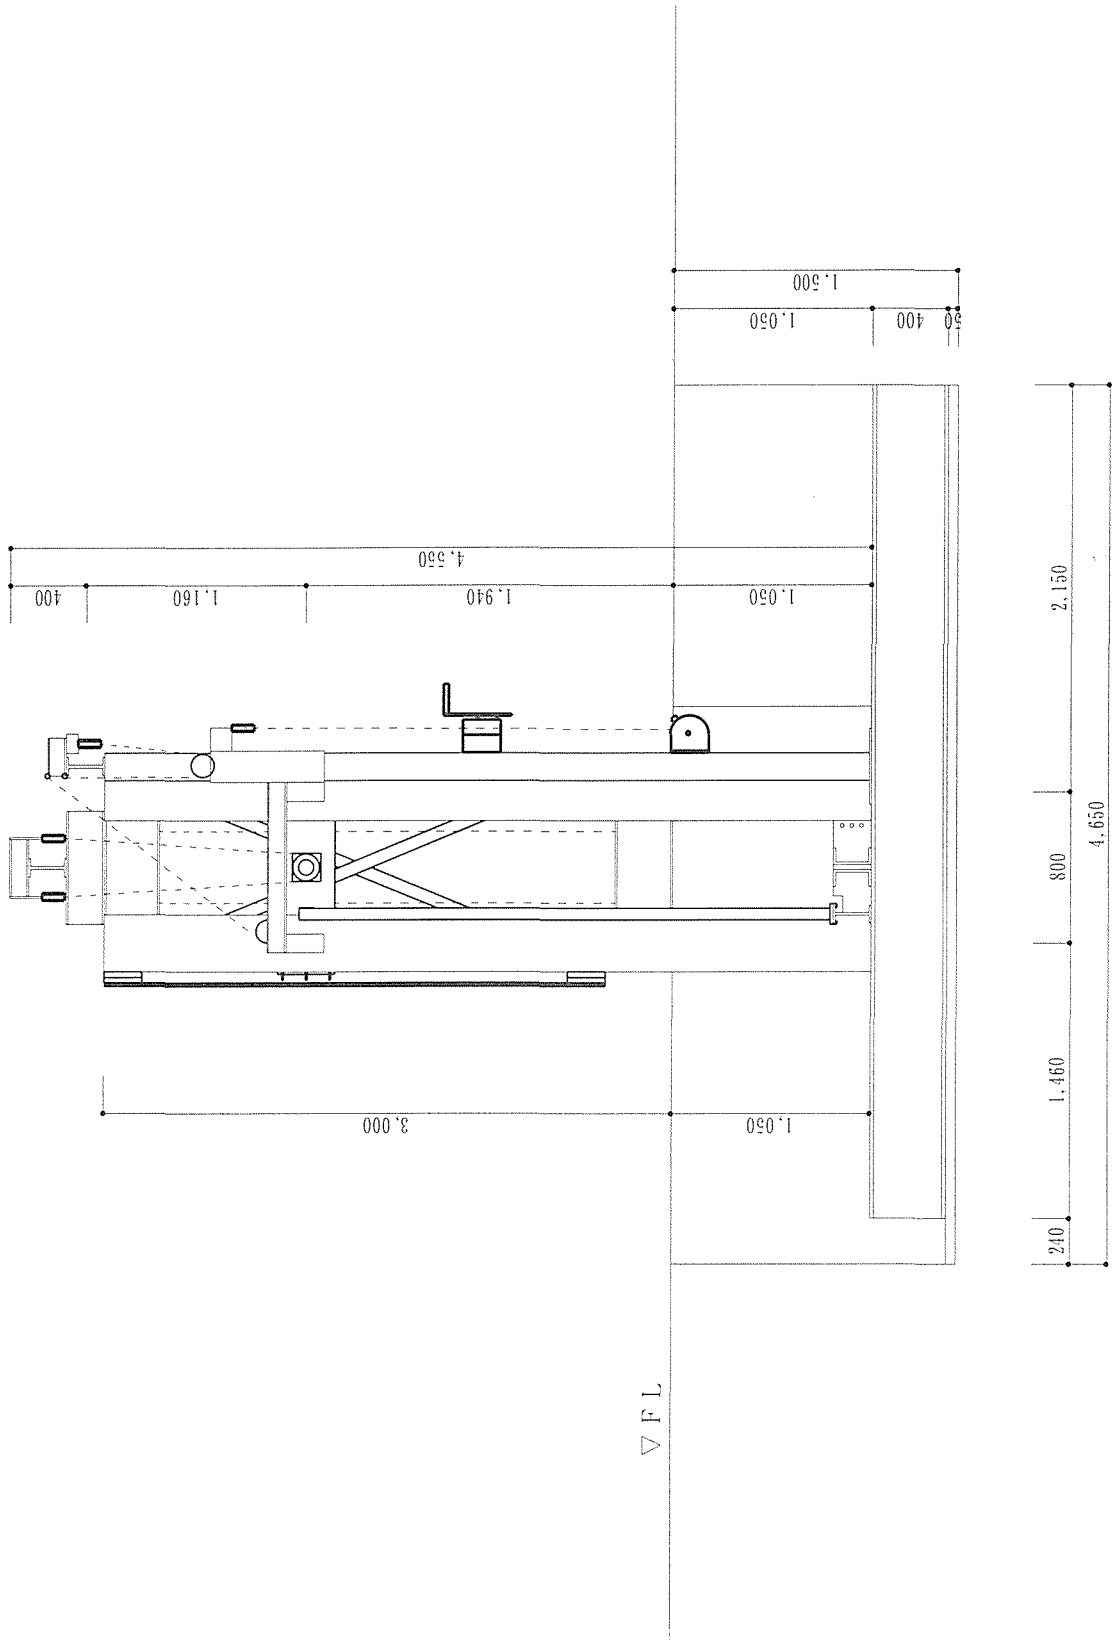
载荷装置 南立面图 S : 1 / 40
